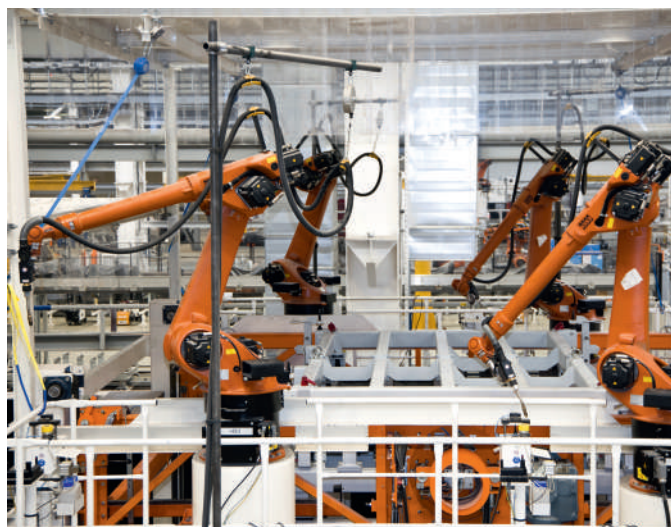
Роботизированная линия сварки торцевых стен вагонов
